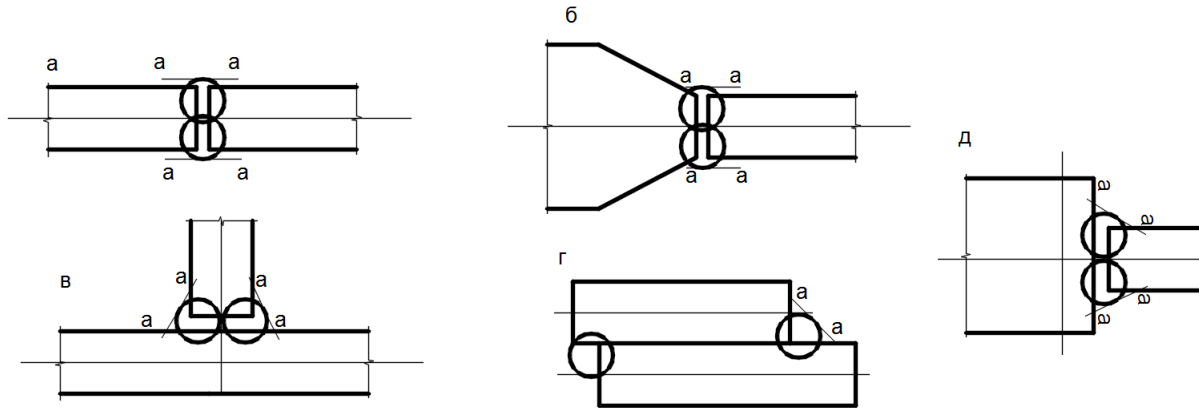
Сварные соединения: а, б- соединения со стыковыми швами; в, г, д- с угловыми.
